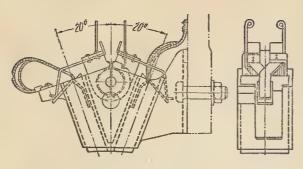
Сдвоенный реактивный щеткодержатель.
